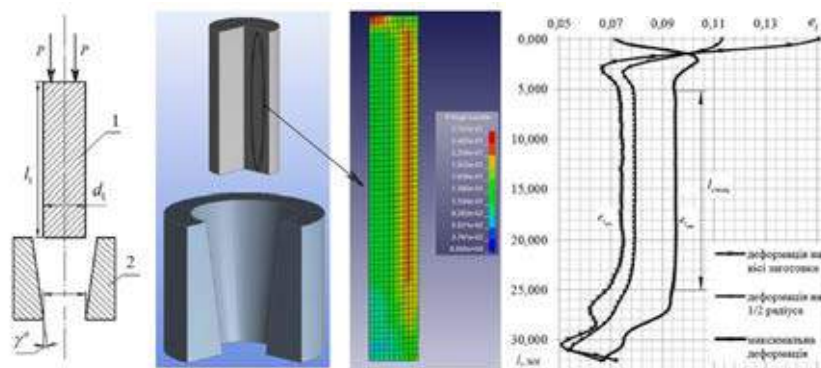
Редукування заготовки (1 – заготовка, 2-матриця)
